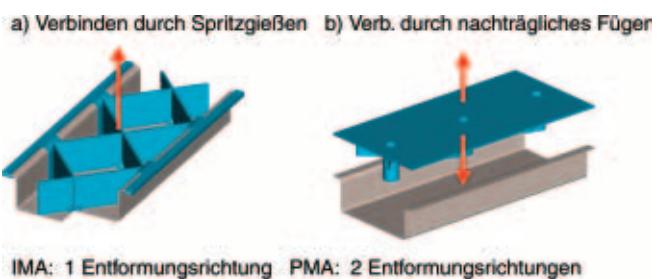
Entformungsmöglichkeiten beim In-Mould Assembly (IMA) und beim Post Moulding Assembly (PMA)
